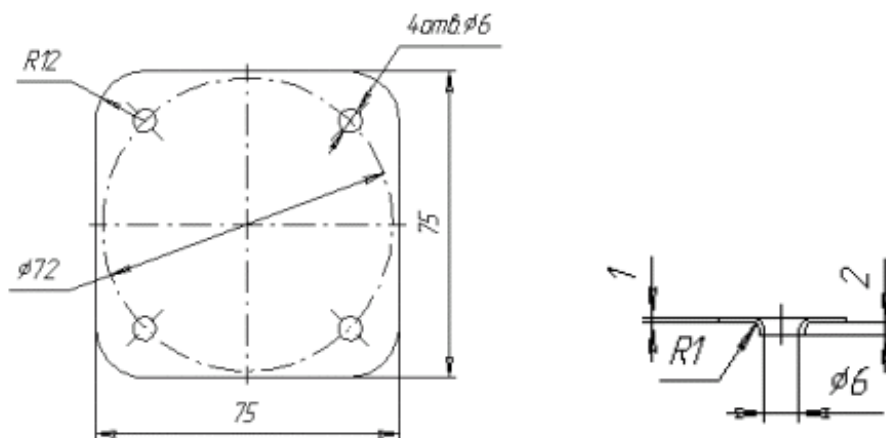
Эскиз детали и разрез отбортованного отверстия
